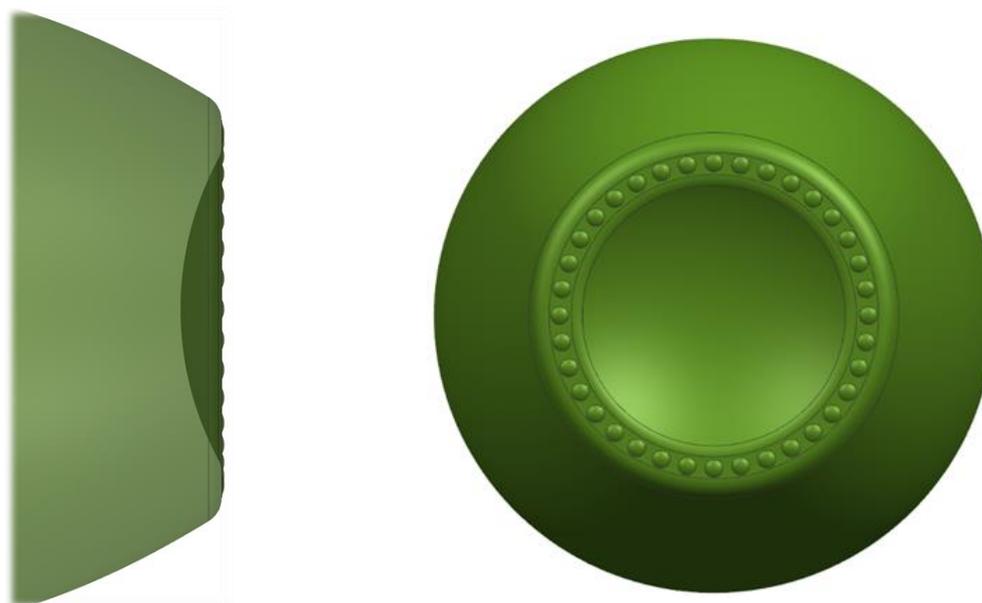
Vista en alzado y planta inferior de la picadura y el estriado en la base de la botella.
